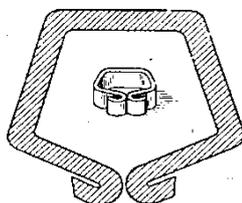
Форма алюминиевой скобы для запечатывания пакета
